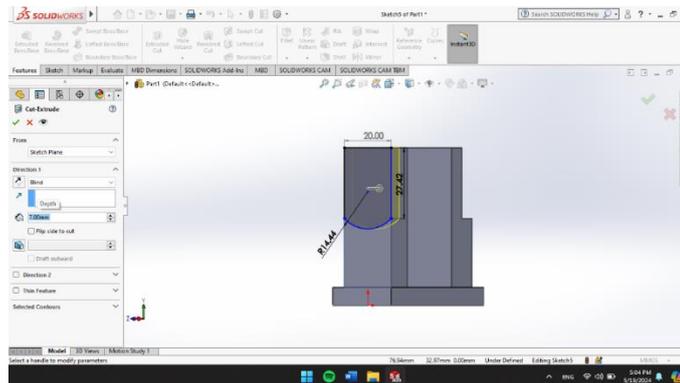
Hasil Extruded Cut Sisi Samping Kiri Pada Upper Base
